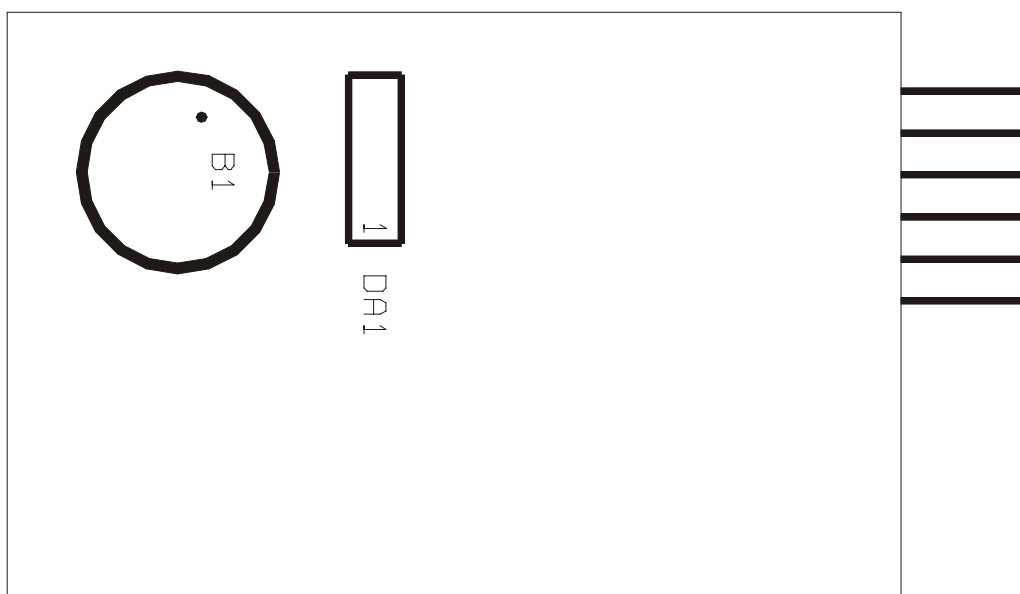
Сборочный чертеж платы управления ФП-12. Сторона пайки.
